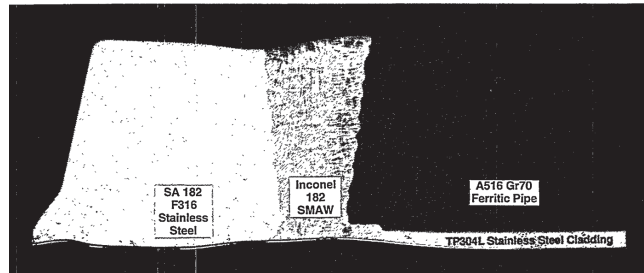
Soudure bimétallique du projet NRC [NRC 95]
